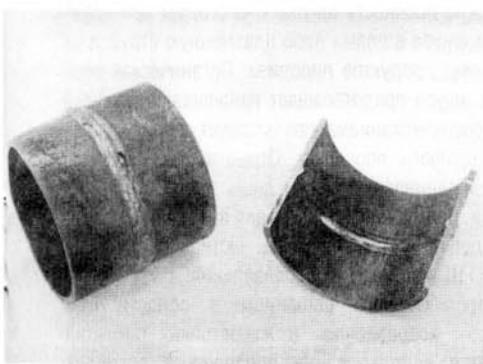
Образцы сварного соединения трубы 89x4 (сталь 20К)
